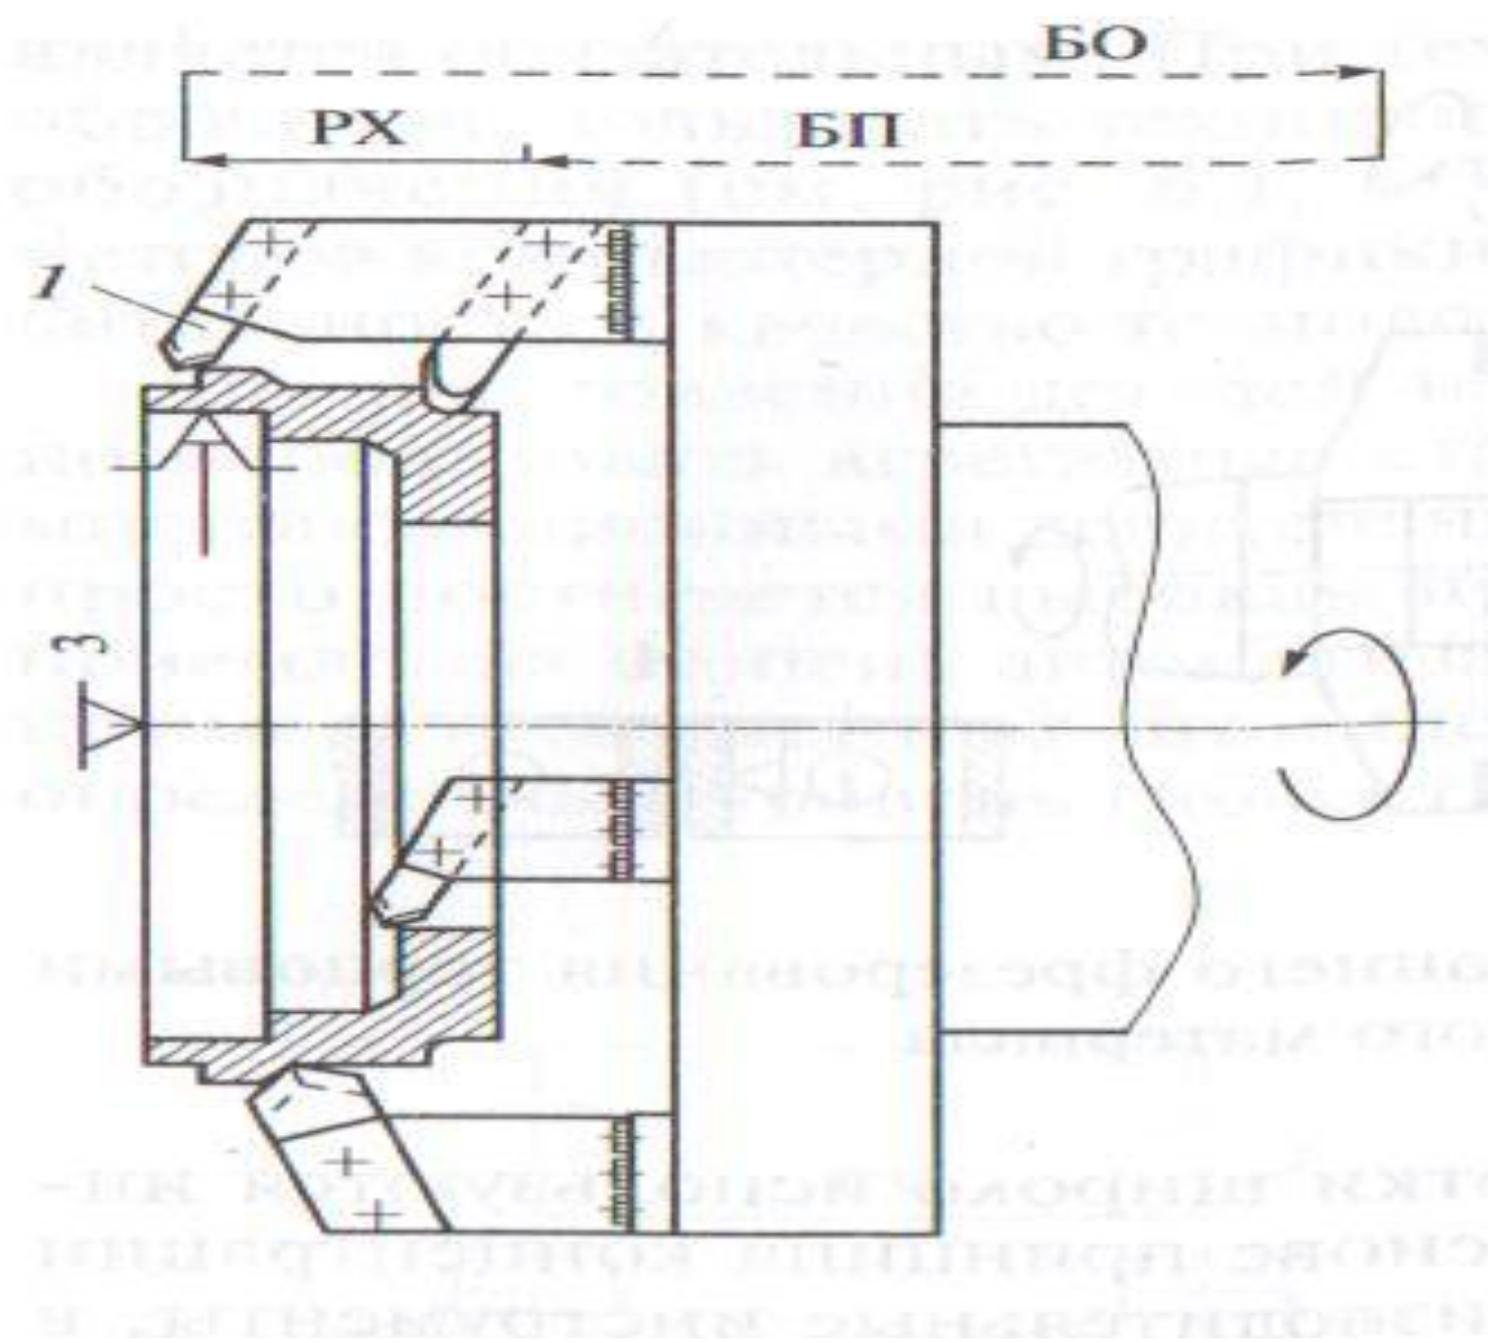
Схема наладки многостороннего фрезерования торцовыми фрезами с пластинами из сверхтвёрдого материала
